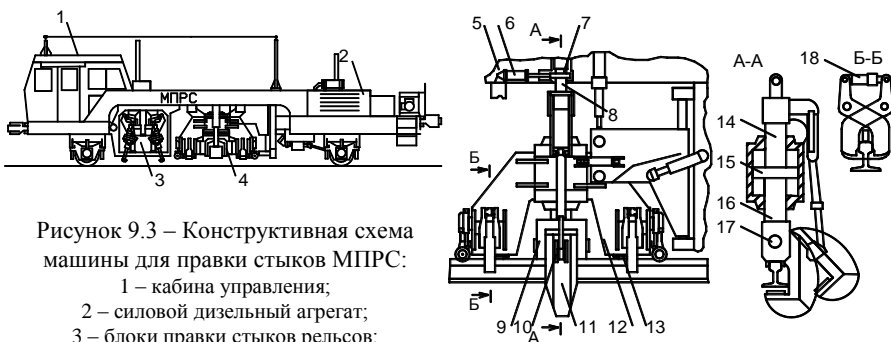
Конструктивная схема машины для правки стыков МПРС:
